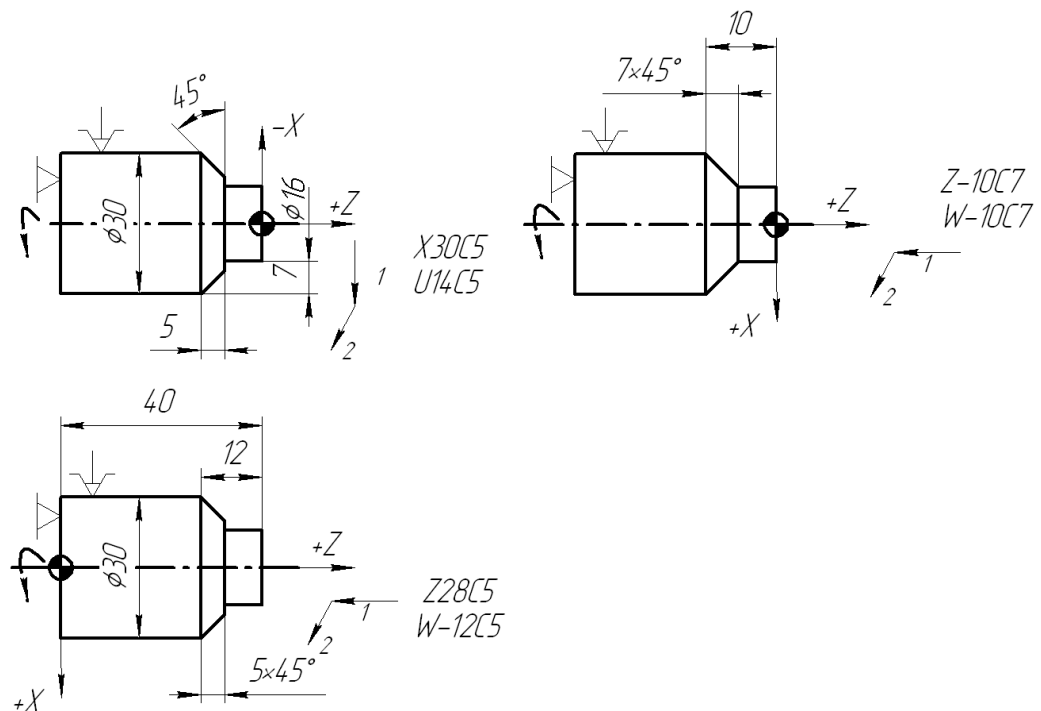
Ескіз обробки деталі зі зворотнім конусом
